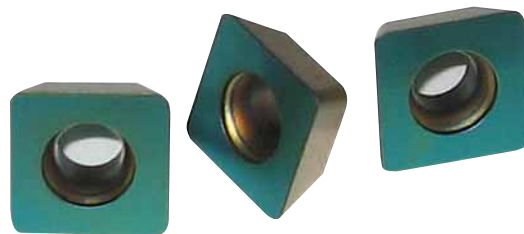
Твердосплавные пластины «СКИФ-М» с новым покрытием для титана
